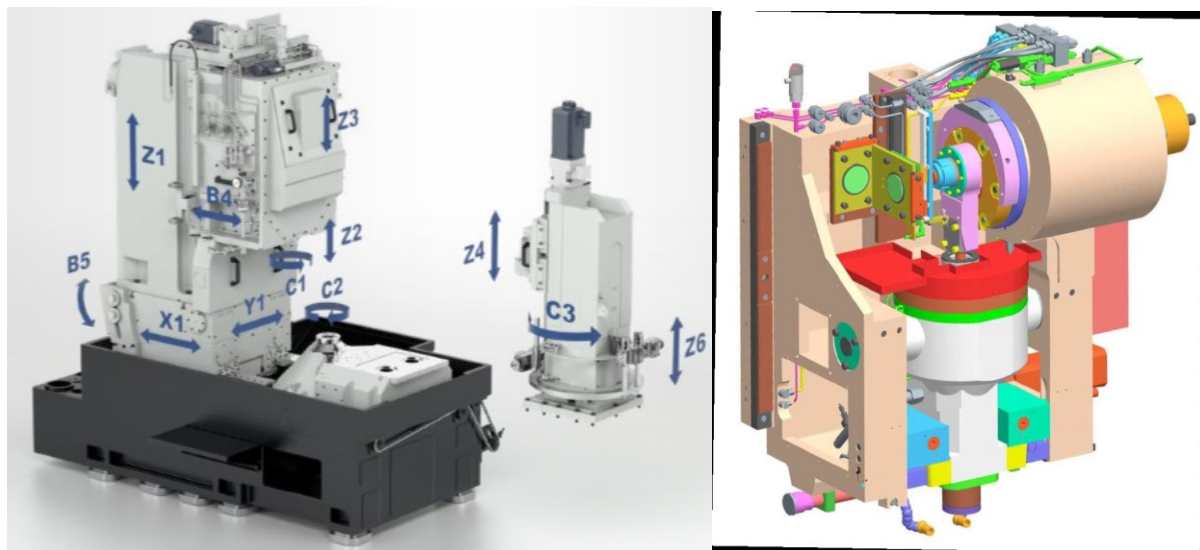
Konstrukce obrážecí hlavy se saněmi obrážecí hlavy [14]
